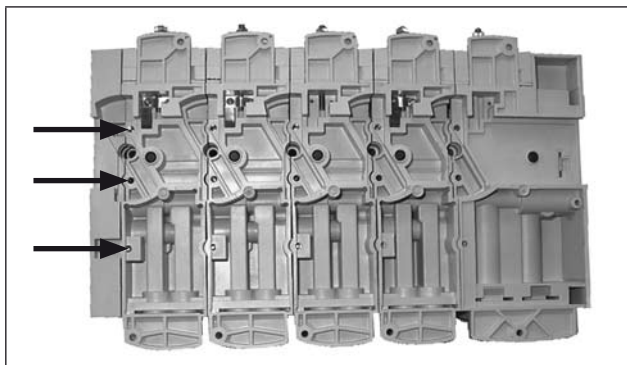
Hilfe beim Entriegeln der Verriegelungsbolzen
